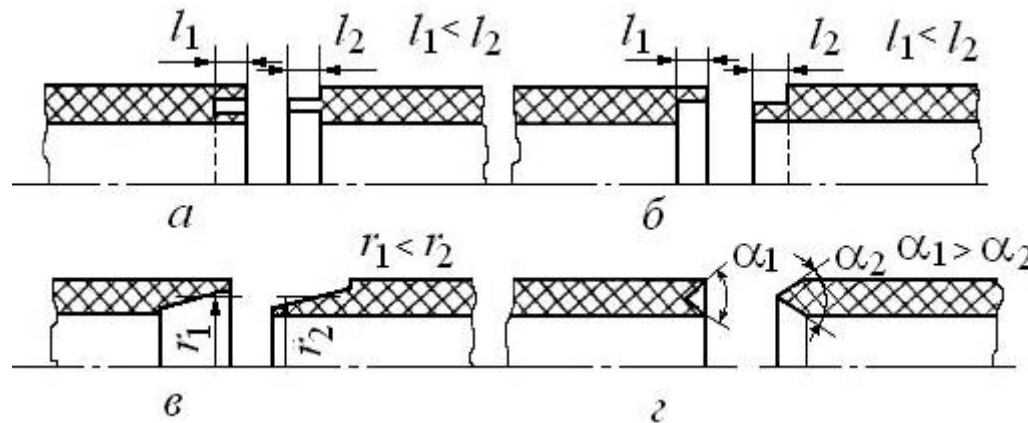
Типы разделки кромок при стыковой сварке труб вращением: а – «шип в паз»; б – уступом; в – «на ус»; г – V – образная
